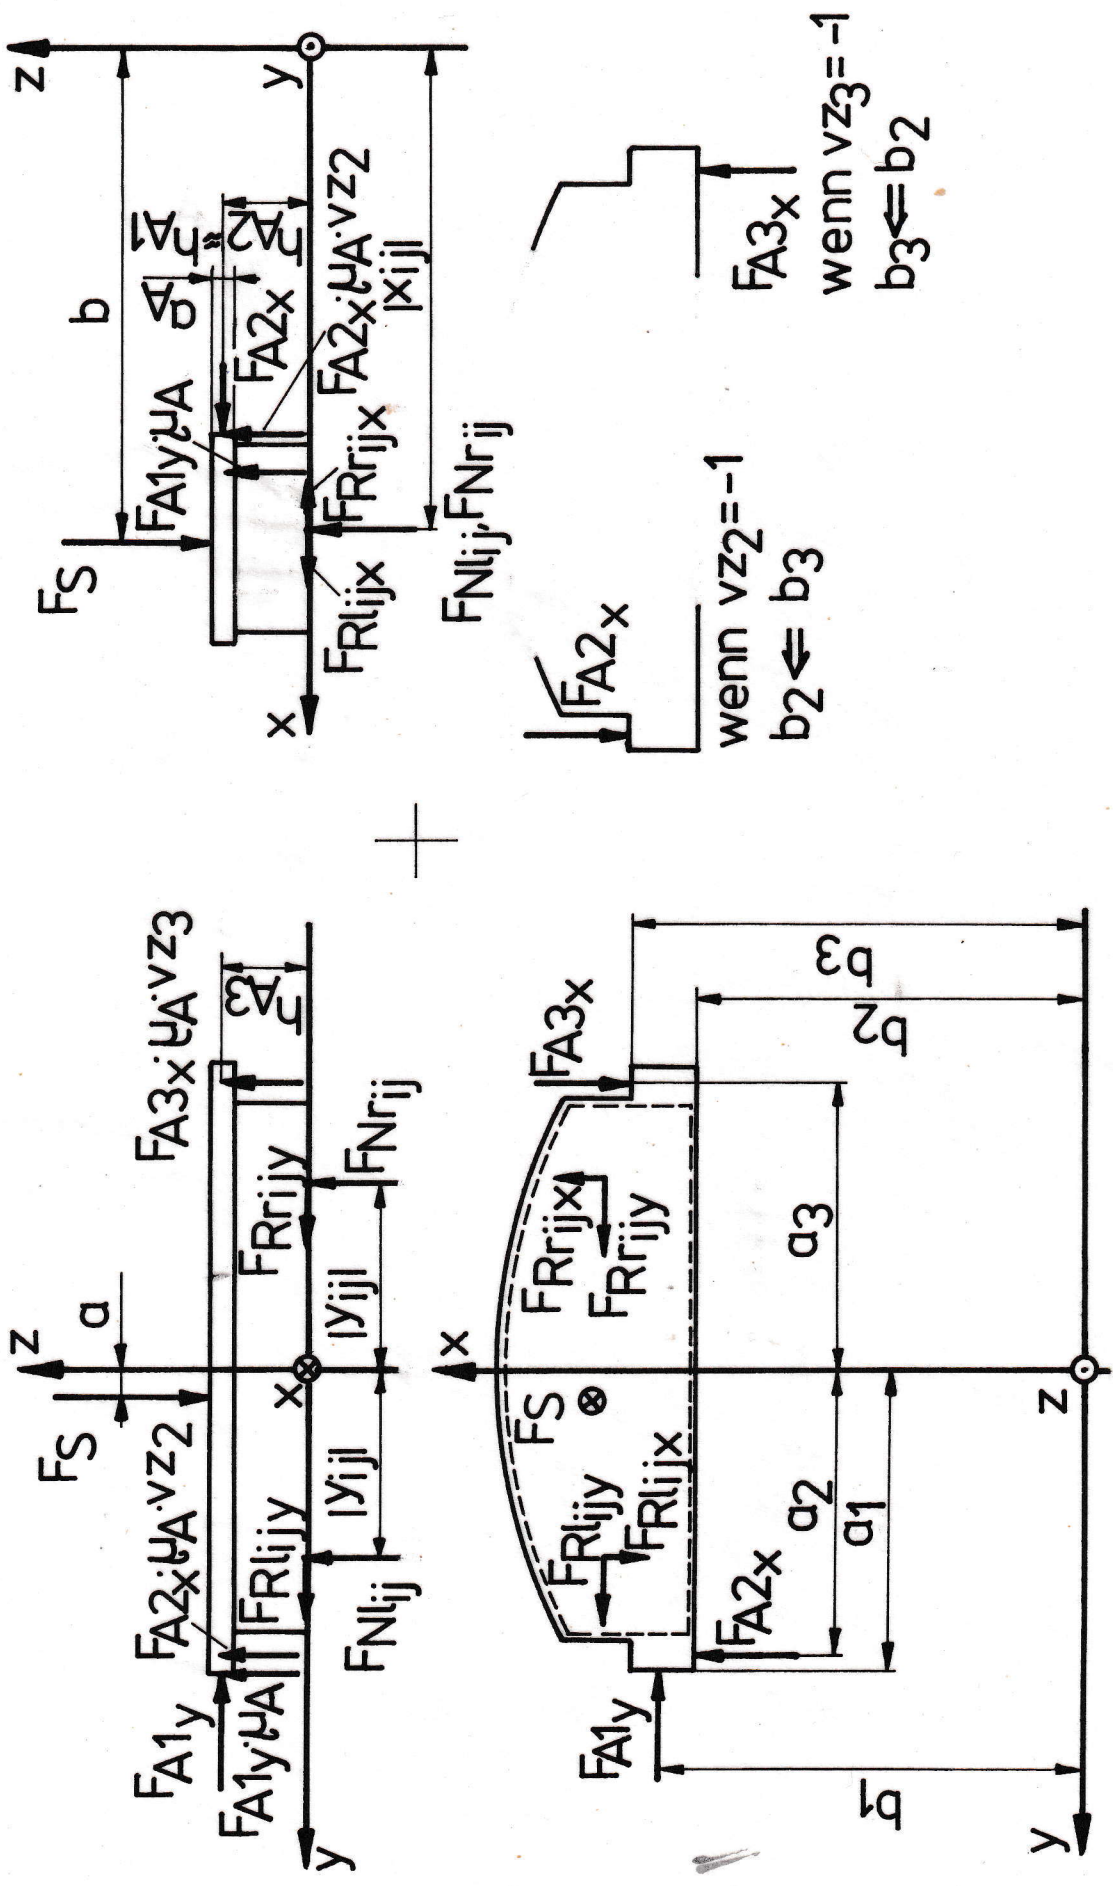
Geschobener Bremsklotz mit einer Hauptabstützstelle
